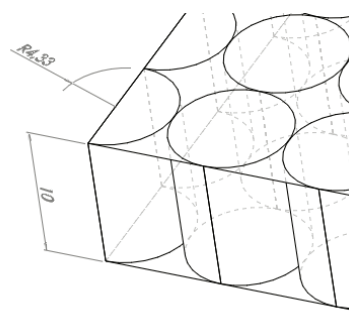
Дискретный наполнитель с круглой формой ячейки
